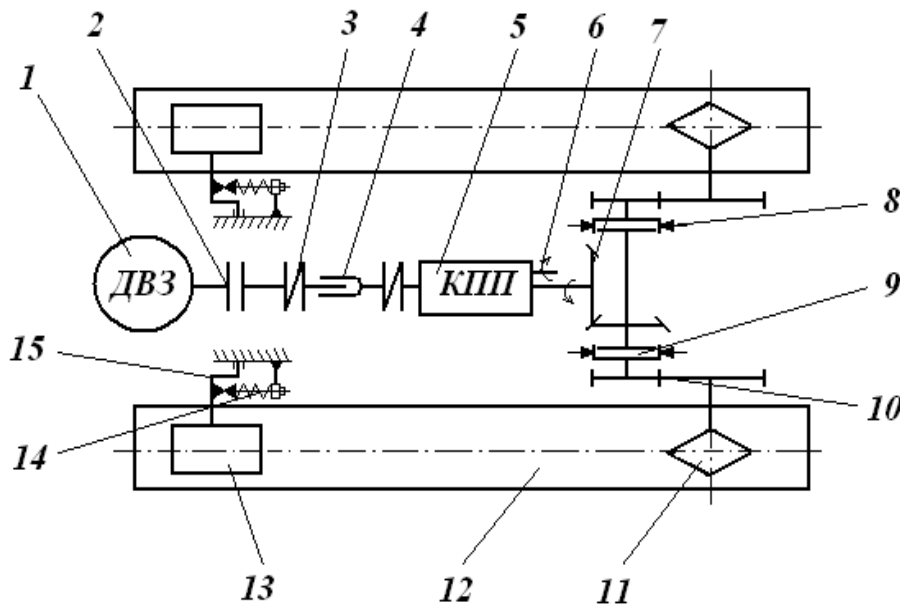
Кінематична схема гусеничного трактора: 1 - двигун внутрішнього згоряння, 2 - муфта зчеплення, 3 - еластична муфта, 4 - телескопічний вал, 5 - коробка переміни передач, 6 - вал відбору потужності, 7 - шестерні центральної передачі, 8 - гальма, 9 - бортовий фрикціон, 10 - шестерні кінцевої передачі (бортовий редуктор), 11 - ведуча зірочка, 12 - гусениця, 13 - натяжне колесо, 14 - пружина, 15 - колінчастий вал
